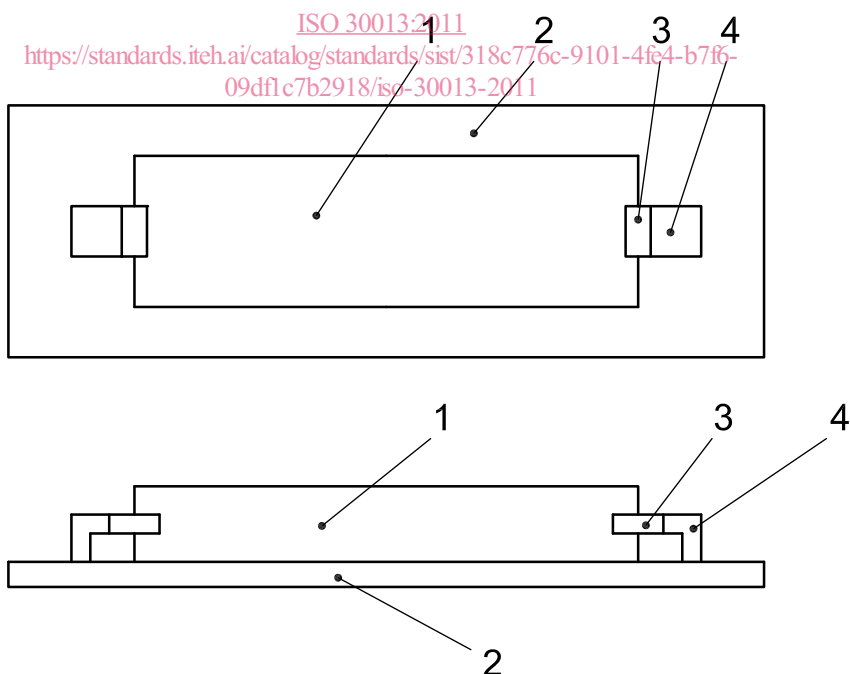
Porte-éprouvettes pour éprouvette de type 2
